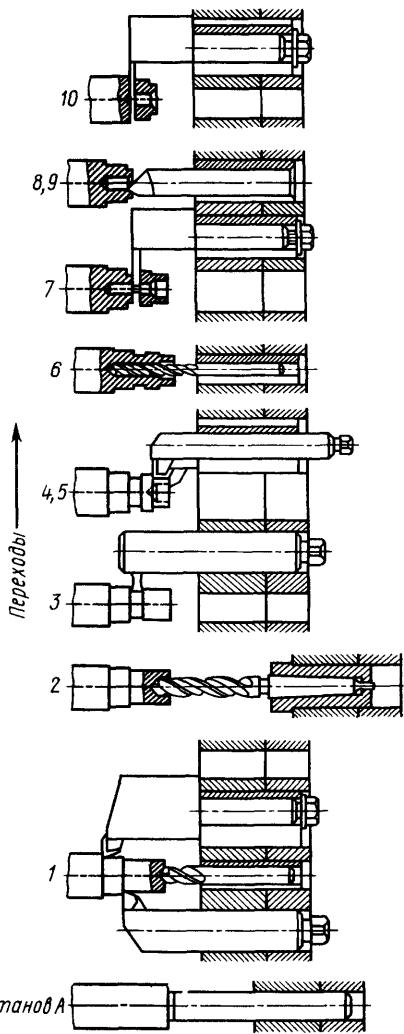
Схема наладки станка с горизонтальной осью револьверной головки для одновременного изготовления двух разных деталей из одного прутка:
